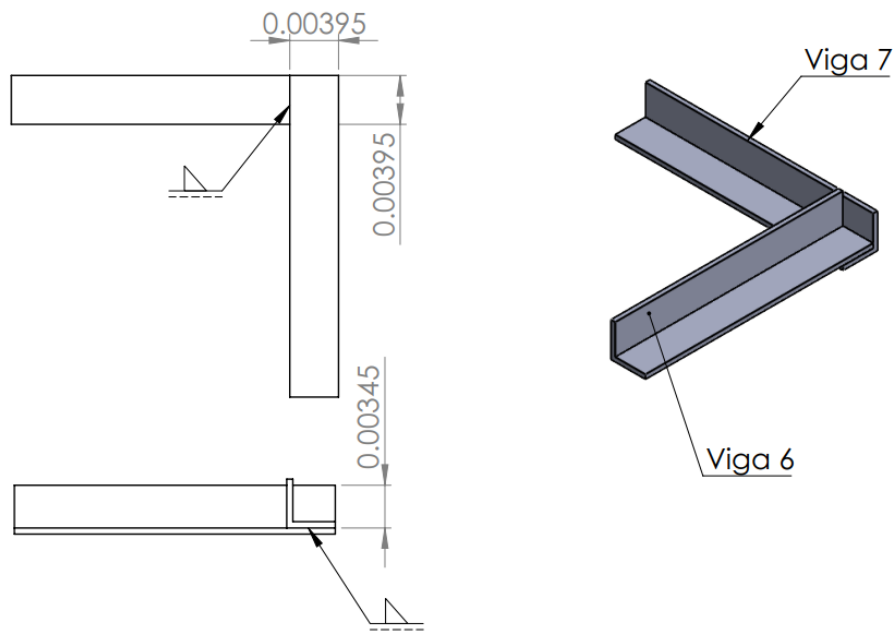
Soldadura entre la viga 6 & 7
